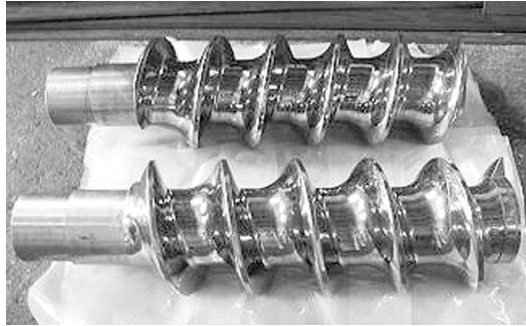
Vis sans fin pour extrudeuse en acier recouverte d'un revêtement multicouches soudable fabriqué par SPS ^[286].
